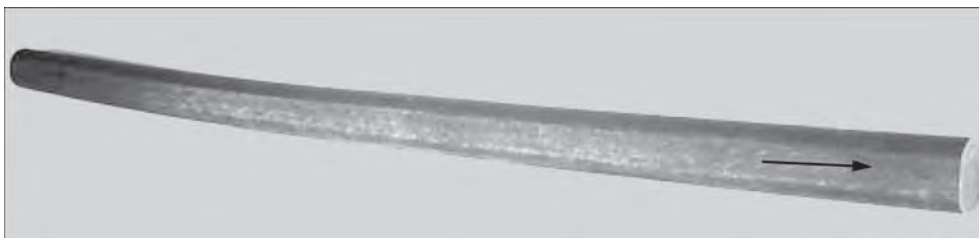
Біметалічний стрижень, отриманий зварюванням вибухом мідної основи зі сталеву трубою
